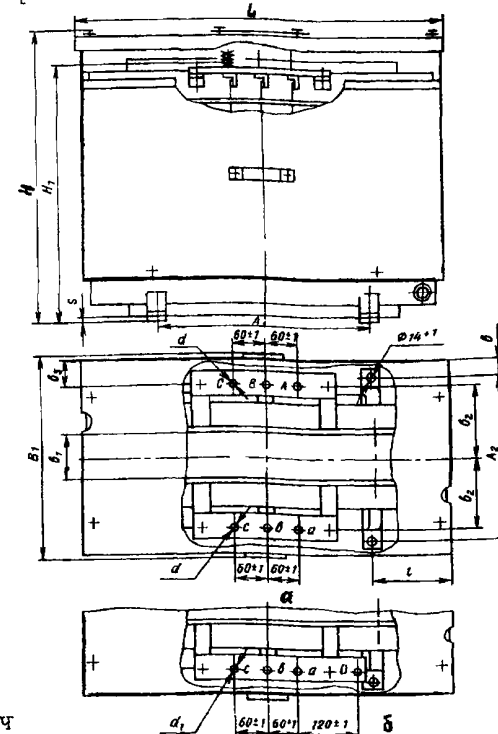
Габаритные, установочные, присоединительные размеры трансформатора ТСЗП
